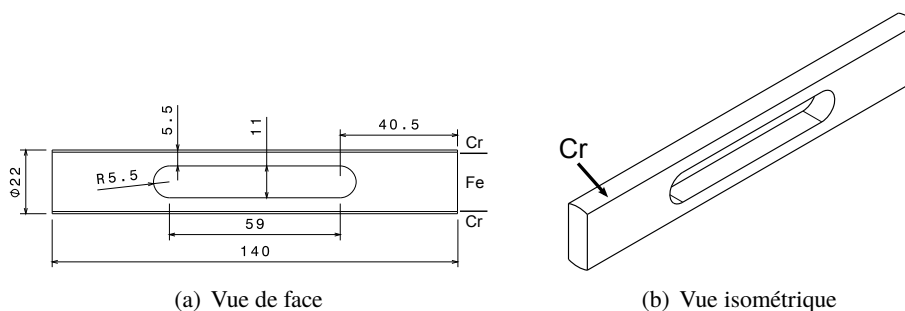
Dimensions des éprouvettes de traction (épaisseur 8 mm)
